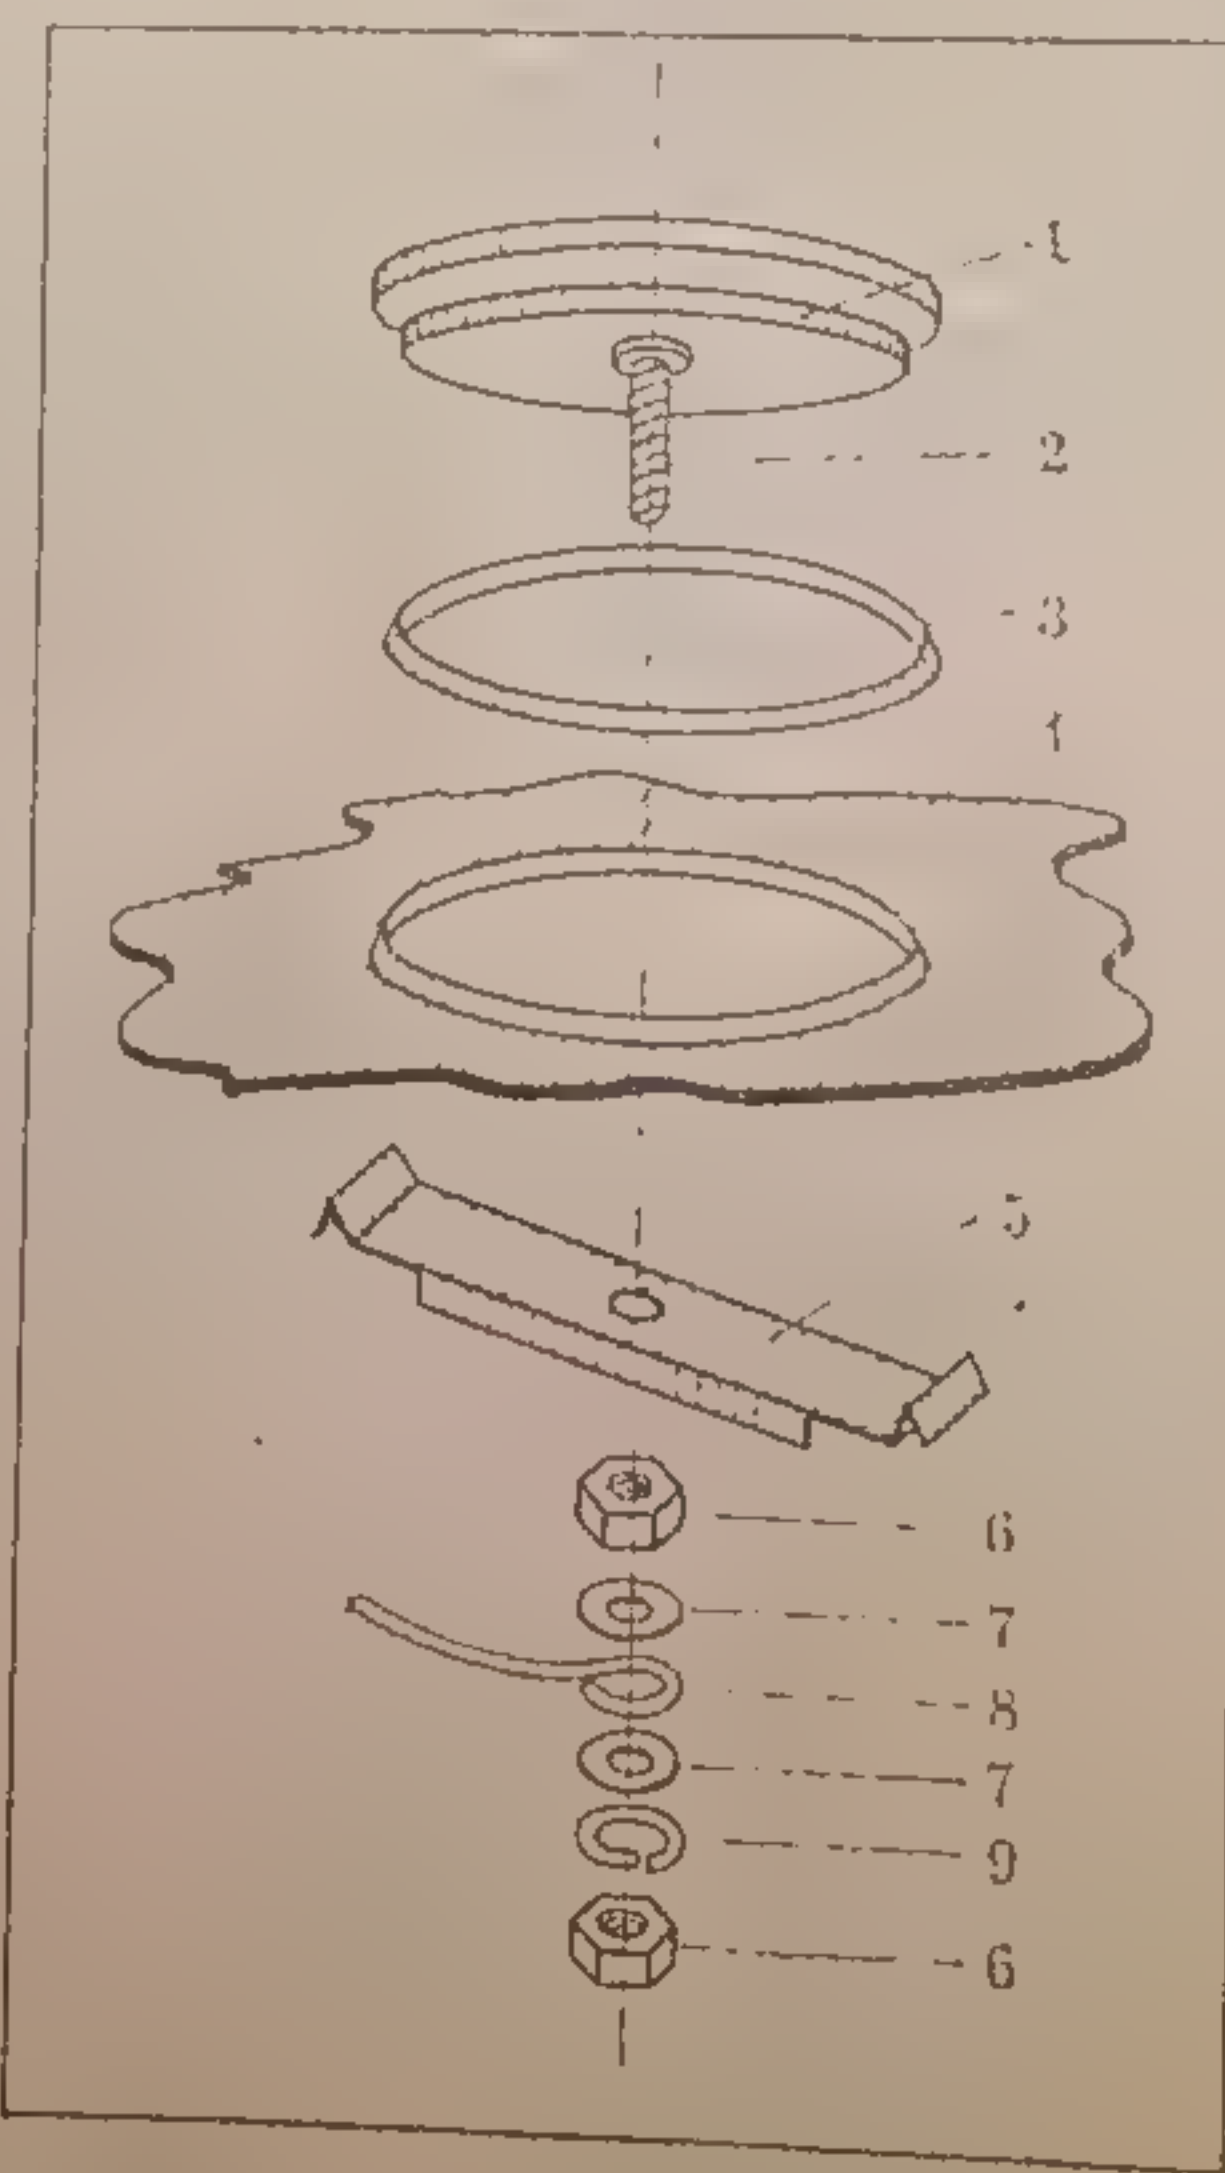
Элементы крепления чугунной конфорки на рабочем столе электроплиты: 1 — конфорка; 2 — шпилька М6х40; 3 — кольцо манжета; 4 — рабочий стол; 5 — скоба; 6 — гайка; 7 — шайба; 8 — заземляющий провод; 9 — пружинная шайба
